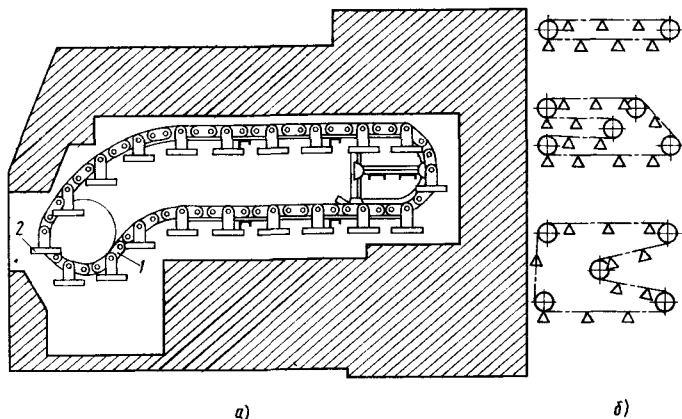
Общий вид (а) и трассы цепей (б) ковшовых конвейеров: 1 — цепь; 2 — люлька
